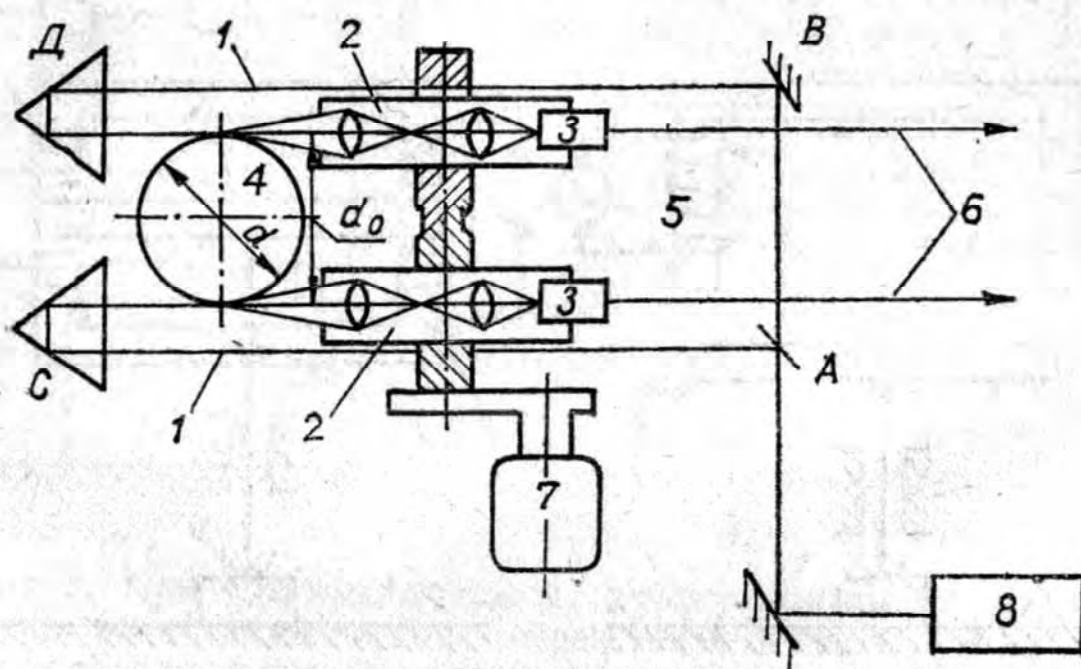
Лазерное устройство для измерения диаметра цилиндрических деталей
